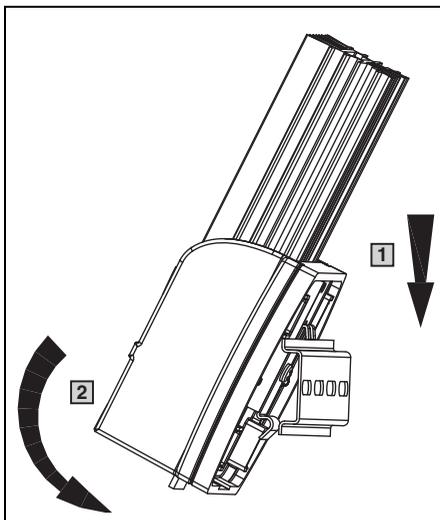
Монтаж при помощи защелкивающегося крепления
